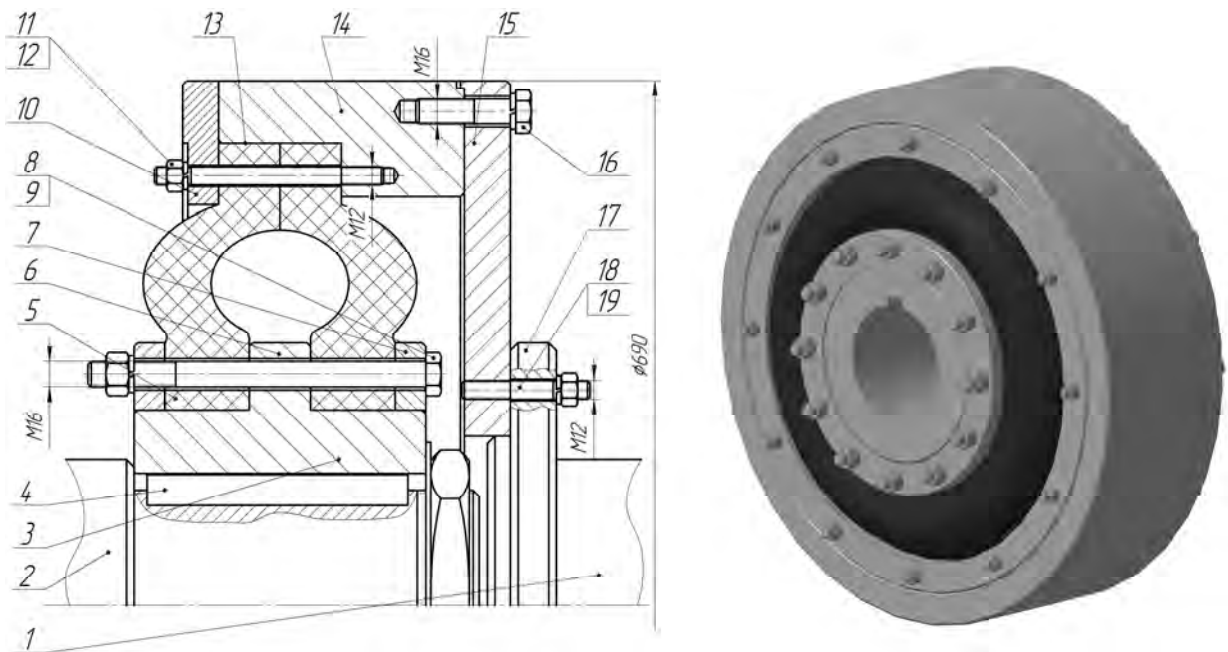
Загальний вид муфти VULKAN EZR 1422, яка сполучає вихідний вал реверс-редуктора та проміжний вал
